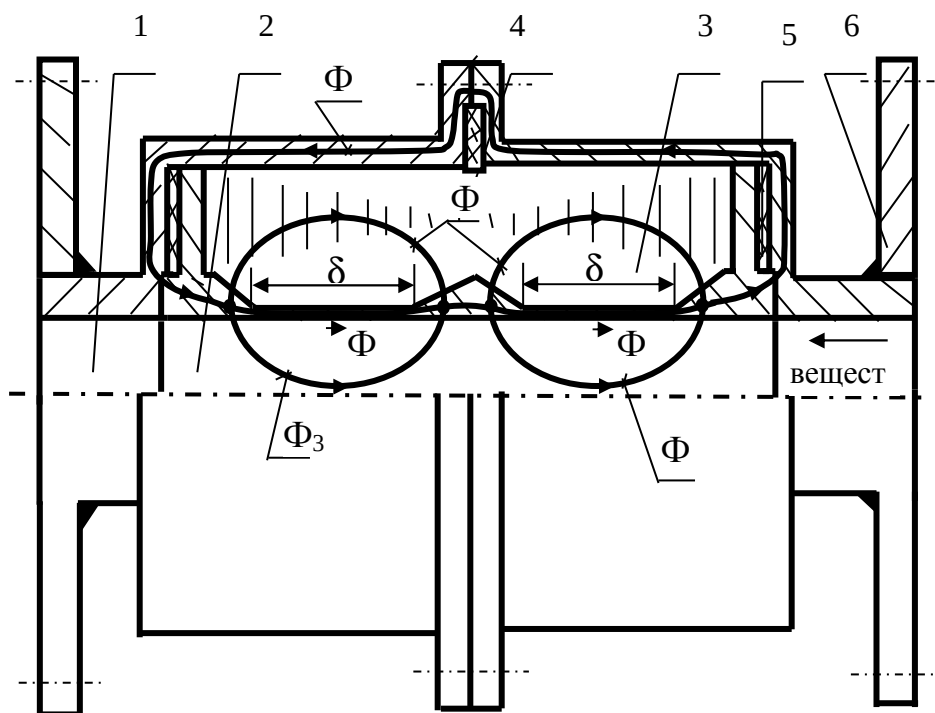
Аппарат магнитной обработки воды: 1 — корпус; 2 — каркас намагничивающей катушки; 6 — фланец; 3 — намагничивающая катушка; 4, 5 — прокладка
